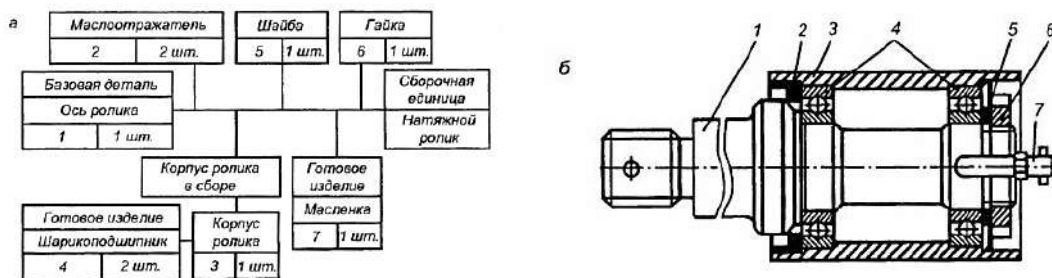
Схема сборки (а) сборочной единицы (б): 1 - ось ролика; 2 - маслоотражатель; 3 - корпус ролика; 4 - подшипники; 5 - шайба; 6 - гайка; 7 - масленка
